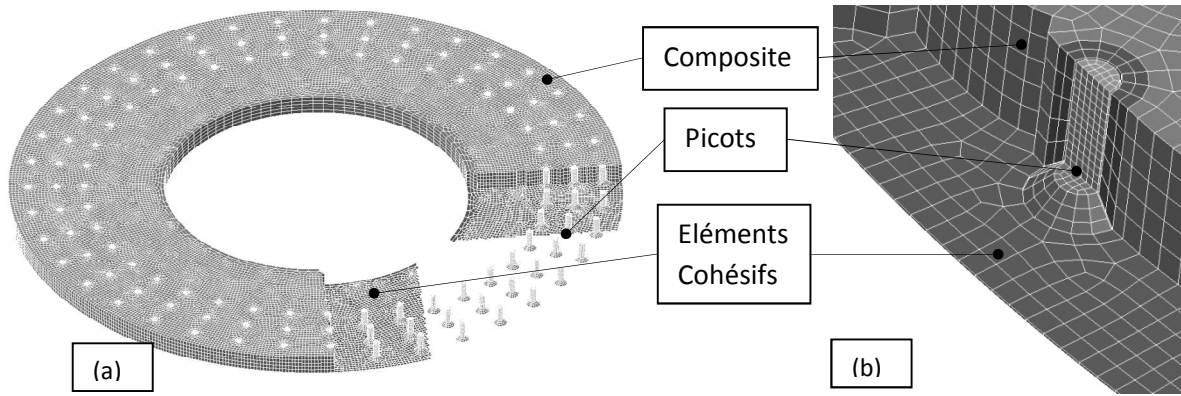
Géométrie & Maillage ; (a) vue d'ensemble, (b) zoom sur un picot et son voisinage
